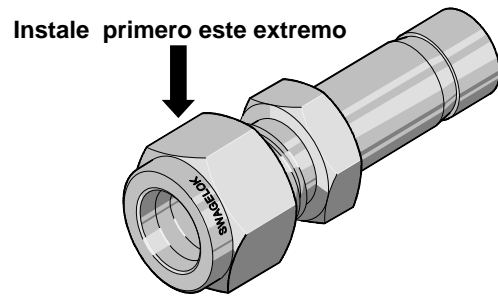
Instale el extremo opuesto a la conexión terminal de adaptador de tubo
